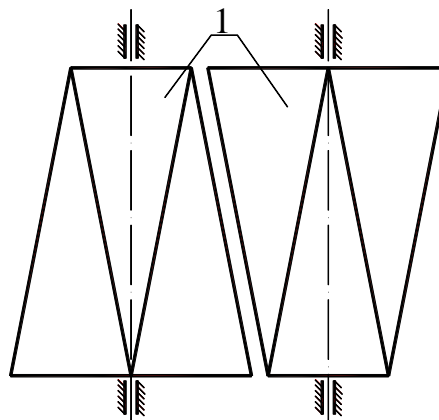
Валковий перероблювальний пристрій з конічною поверхнею валків 1:
